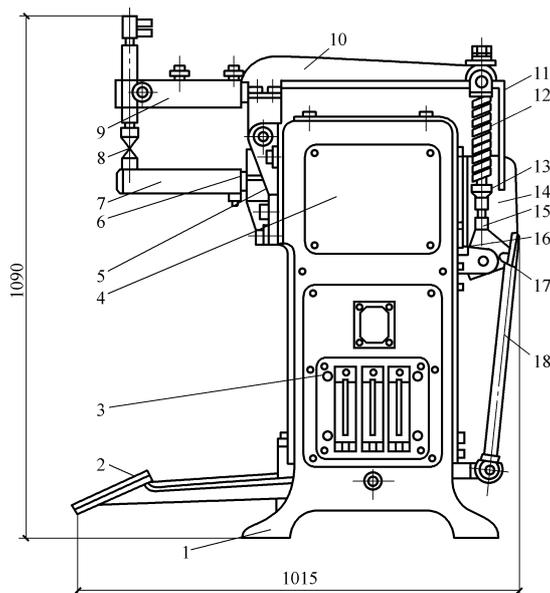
杠杆弹簧式点焊机外形结构
